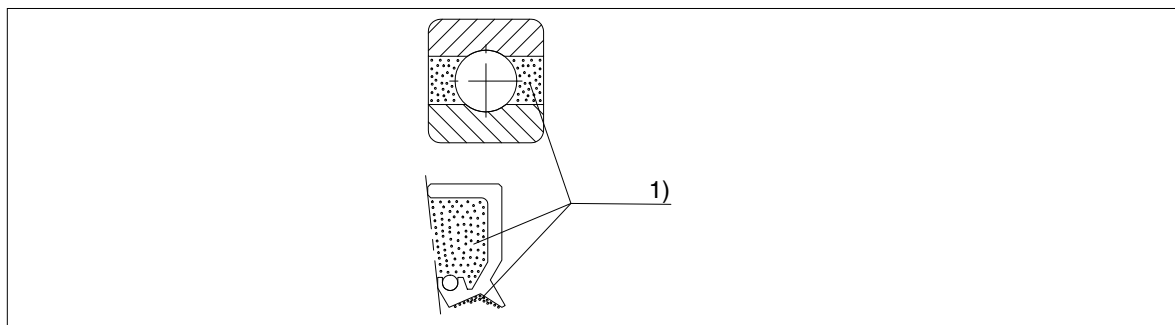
Смазать консистентной смазкой подшипники качения и сальники
